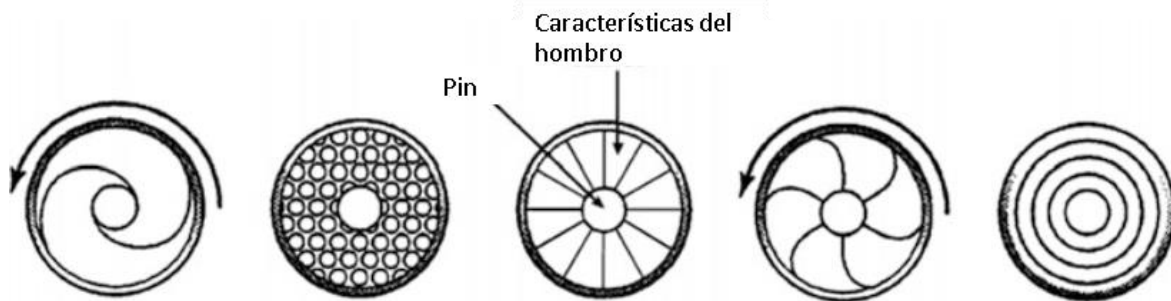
Geometrías del hombro de la herramienta, vista inferior.
